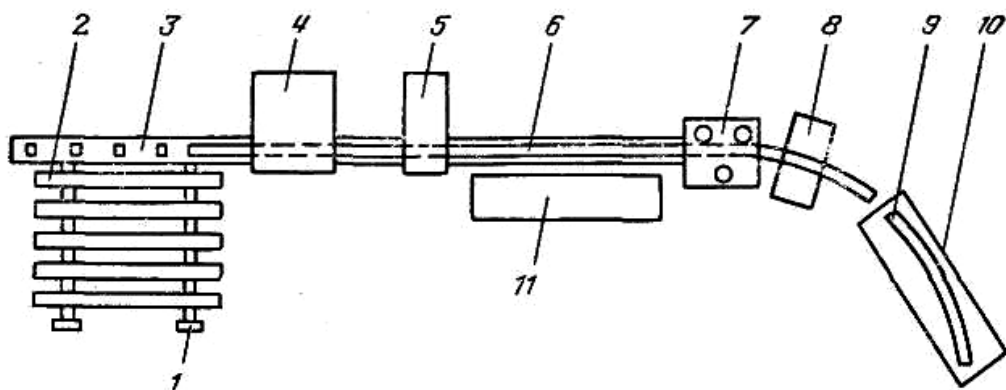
Схема технологічної (безвідходної) лінії виробництва металевого кріплення: 1 - стійка; 2 - спеціальний профіль; 3 - конвеєр (роликовий); 4 - апарат для зварювання; 5 - прес для зрубу прямолінійних елементів; 6 - зварні стрижні профілю; 7 - машина для гнуття; 8 - верстак для елементів; 9 - готове кріплення; 10, 11 - пакувальники криволінійних і прямолінійних елементів
